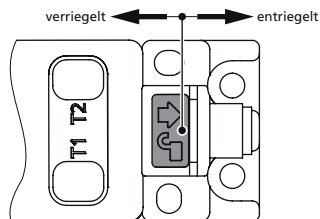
QuickLock-Montagehalterung; Sensor verriegeln/entriegeln
